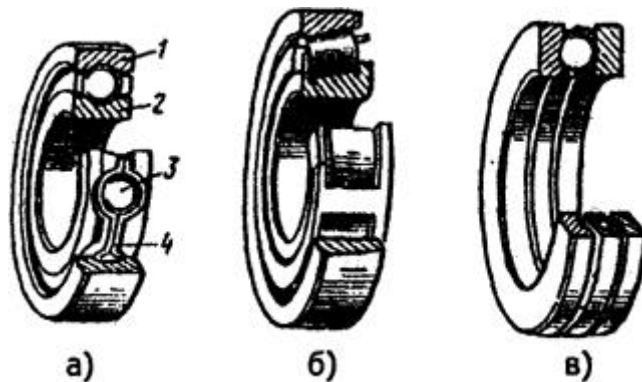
Подшипники качения: а - шариковый радиальный однорядный, б - роликовый конический радиально-упорный, в - шариковый упорный одинарный
